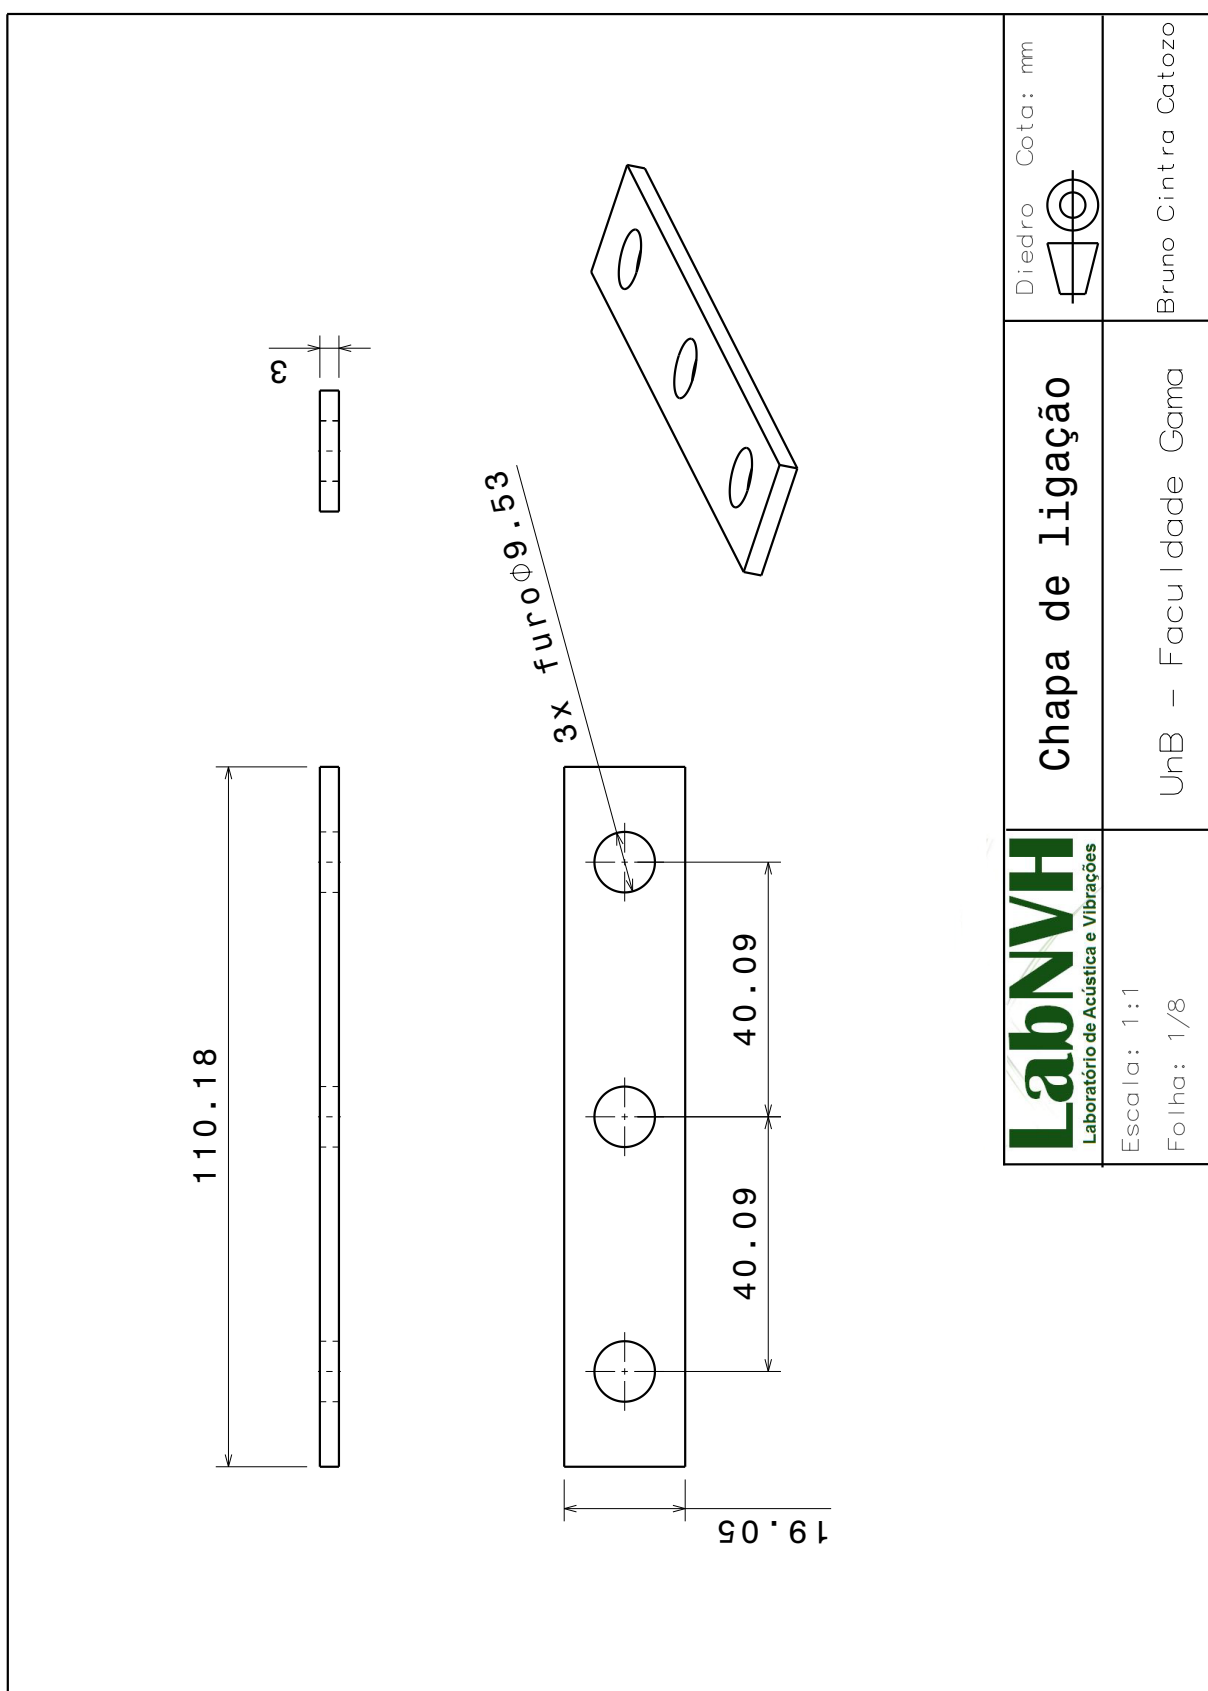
Desenho técnico da chapa de alumínio com 3 mm de espessura
